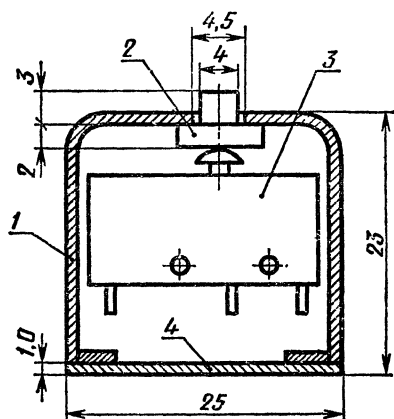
Конструкция кнопки: 1 — корпус (алюминий); 2 — головка кнопки (органическое стекло); 3 — микровыключатель МП-11; 4 — основание
